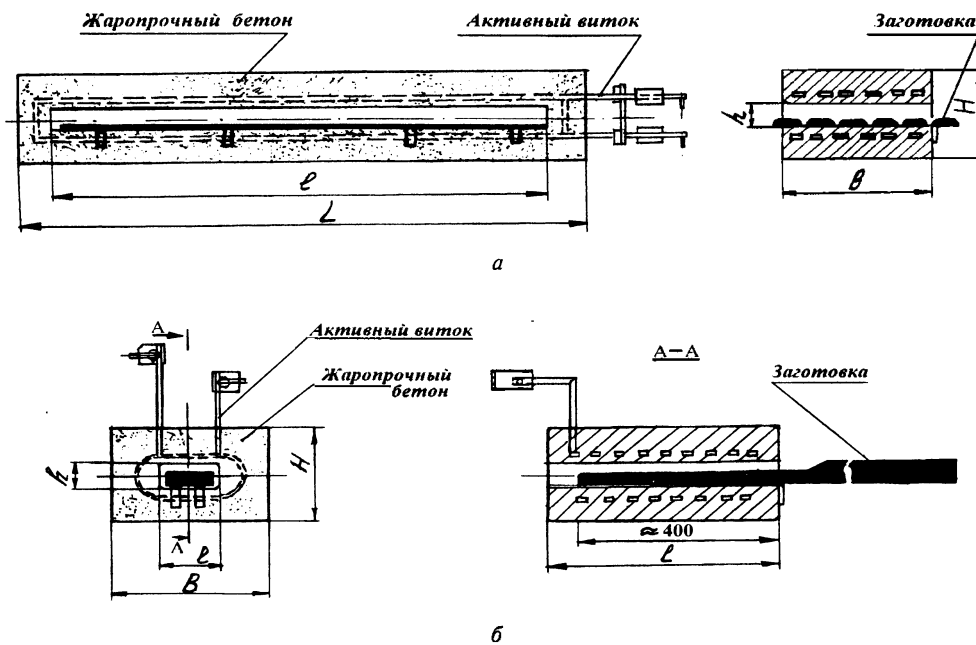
Индукторы для нагрева заготовок рессорных листов: а — под прокатку; б — под навивку
